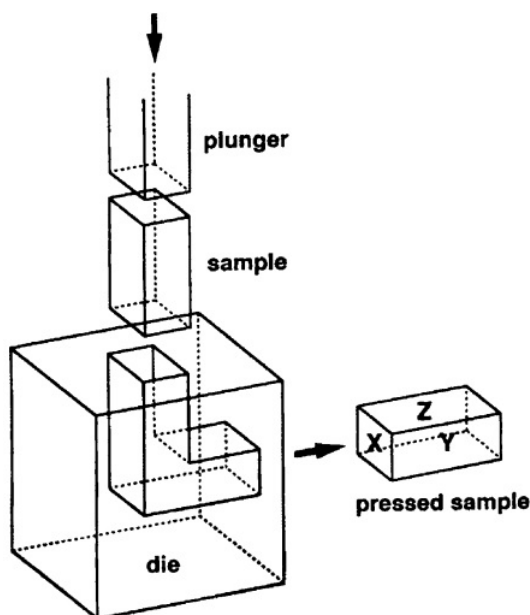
Schéma d'un ECAP typique: les plans X, Y et Z désignent respectivement le plan transversal, le plan d'écoulement et le plan longitudinal[54].
